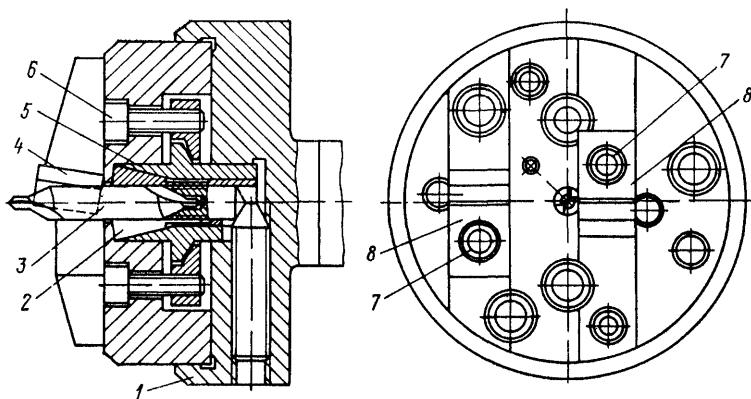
Патрон для подрезки и одновременной зацентровки торцов заготовок
